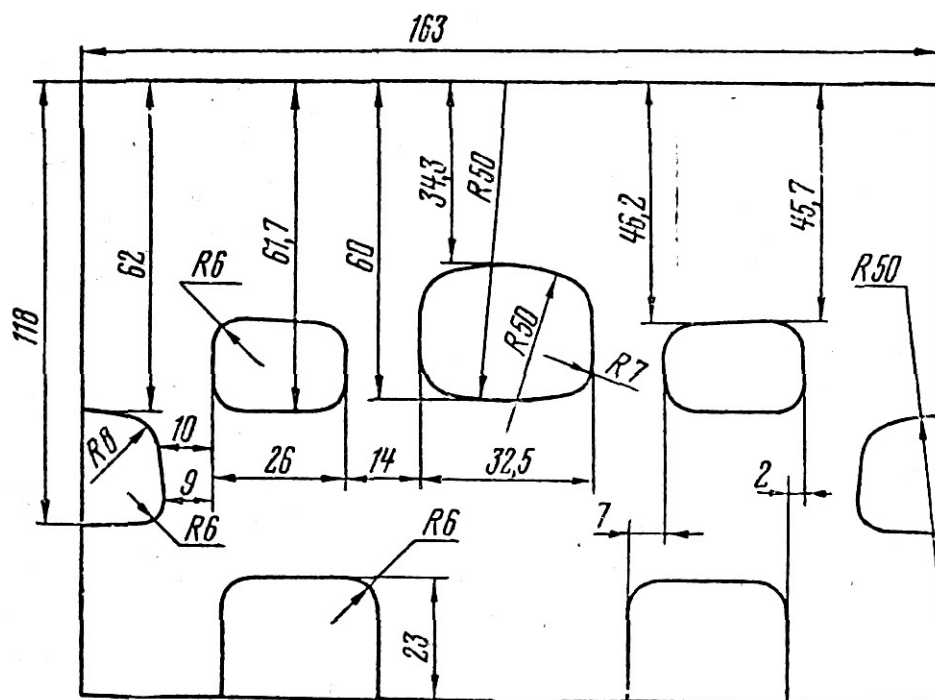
Развёртка цилиндра форсированного двигателя 3.115
